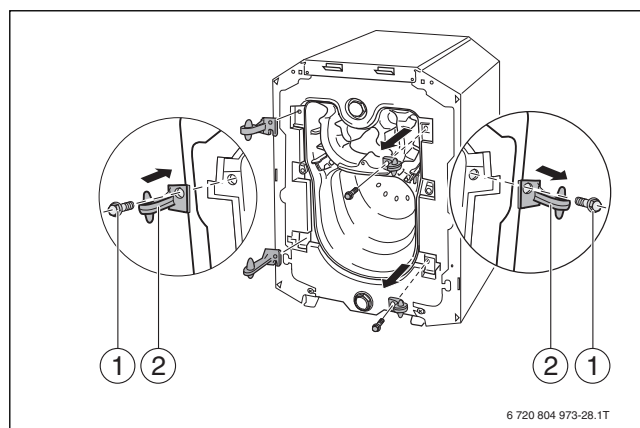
Перестановка двери камеры сгорания (детали котлового блока)
